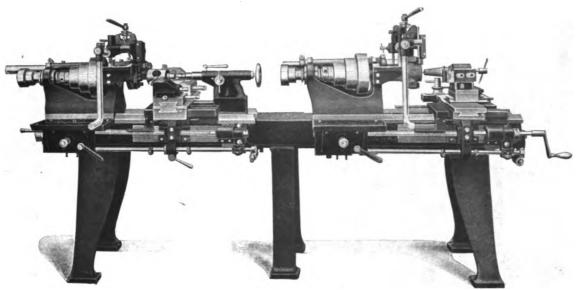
Selbsttätige Doppeldrehbank für Hahngehäuse und Hahnküken von Auerbach & Co., G. m. b. H., Dresden.
